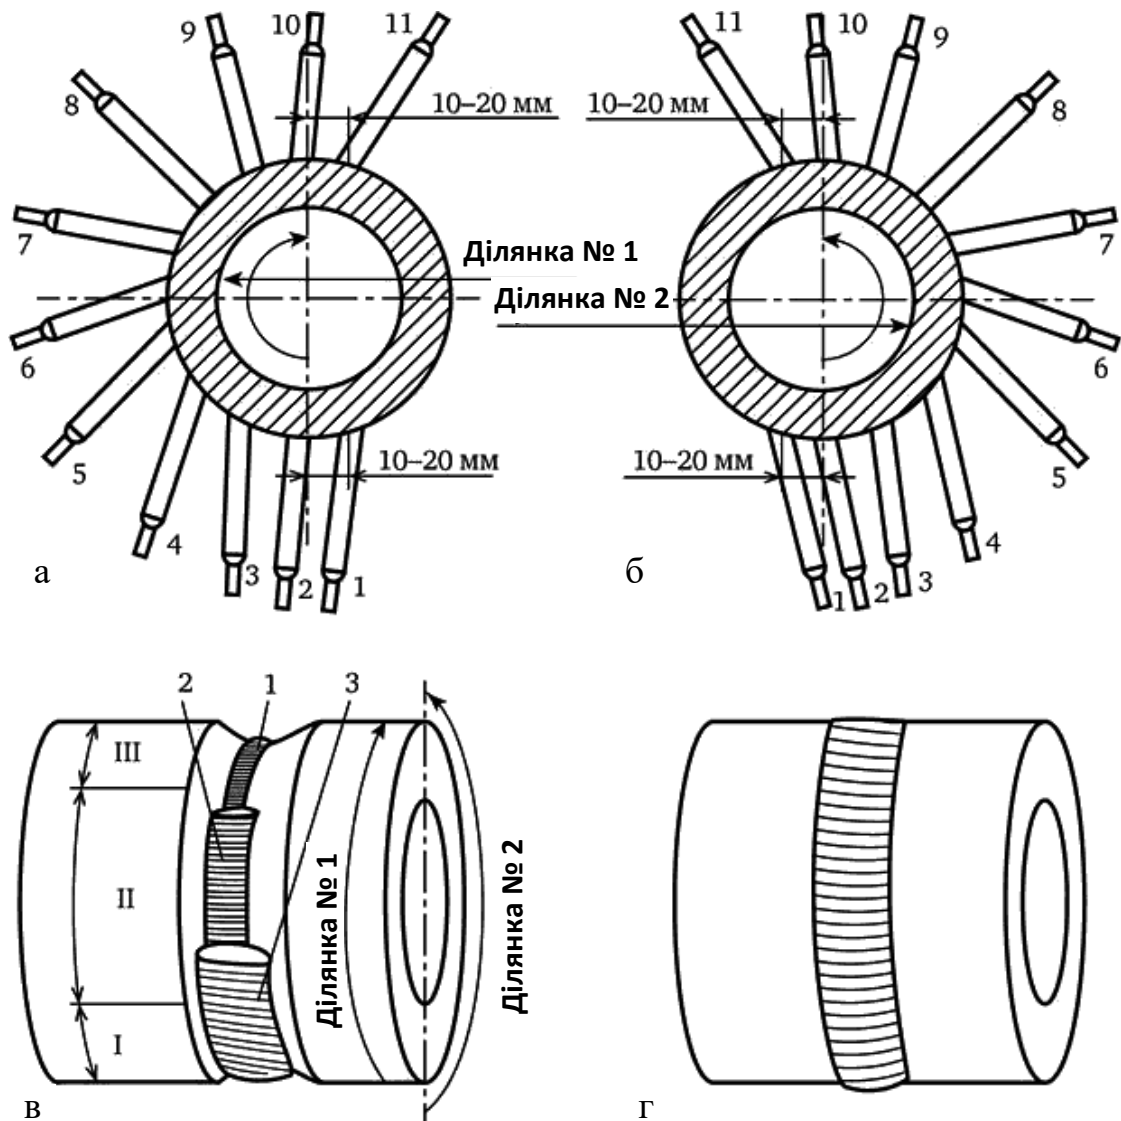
Зварювання неповоротного стику при горизонтальному розташуванні труби: а – робота на першій ділянці; б – робота на другому ділянці; в – зварювання кореневого валика; г – зварювання лицьового шару
